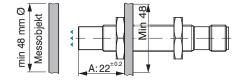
Montage, Abmessungen in mm (nicht maßstabsgetreu)
